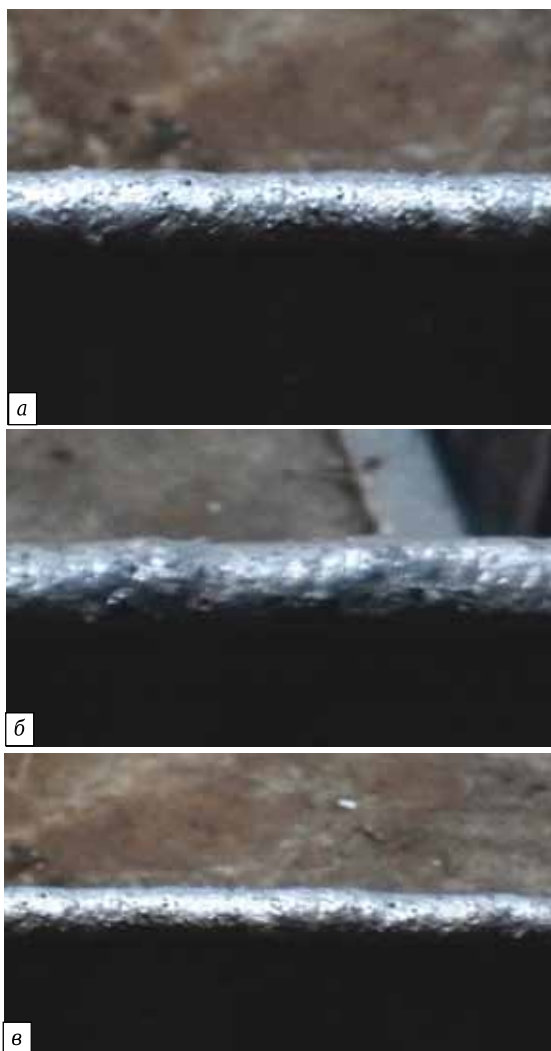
Общий вид неокисленной зоны: а — при наплавке и защите газопорошковой смесью; б — при наплавке и защите газопорошковой смесью и защите только одним газом; в — общий вид защитной зоны при плазменной наплавке газопорошковой смесью
